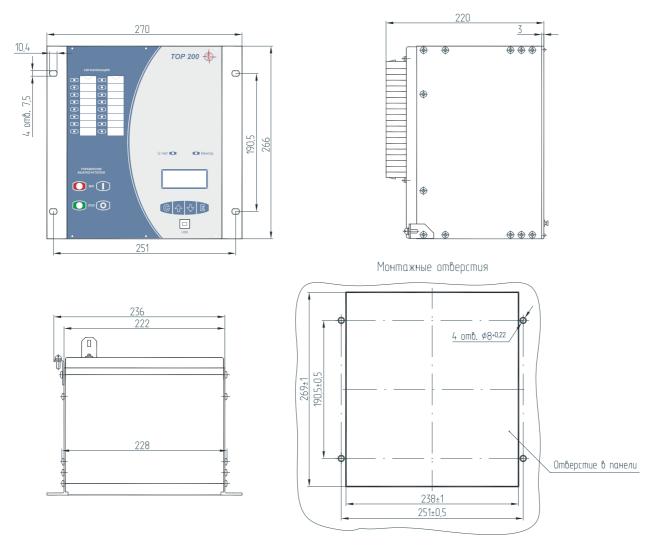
Габаритные и установочные размеры для утопленного монтажа
